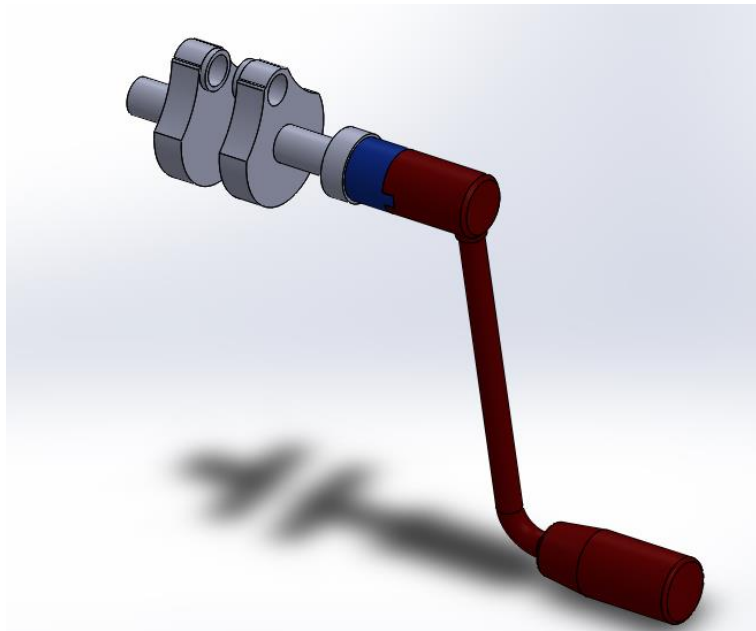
Ensamblaje de la manivela sobre el cigüeñal
